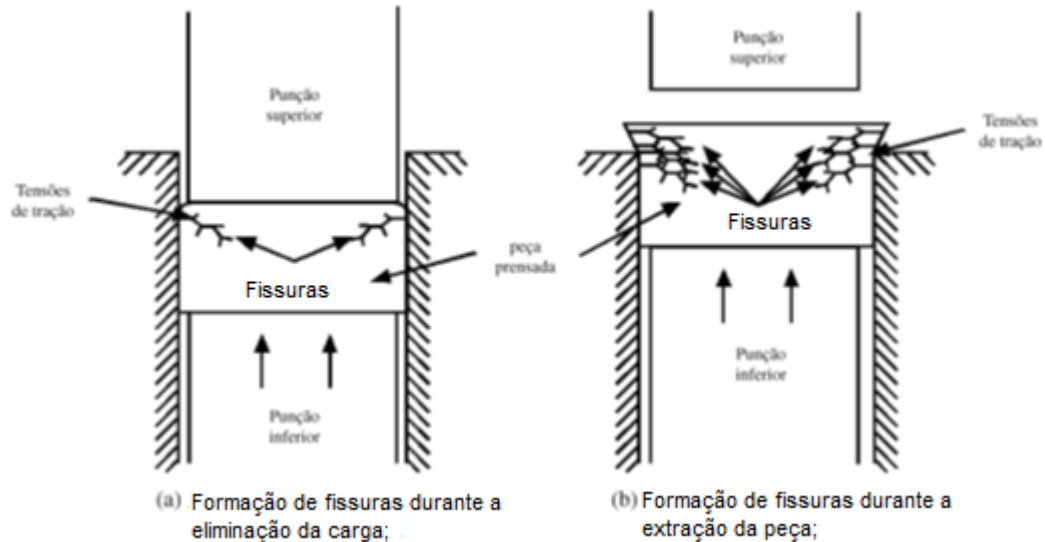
Aparecimento de fissuras durante a etapa de prensagem de uma peça. [6].
